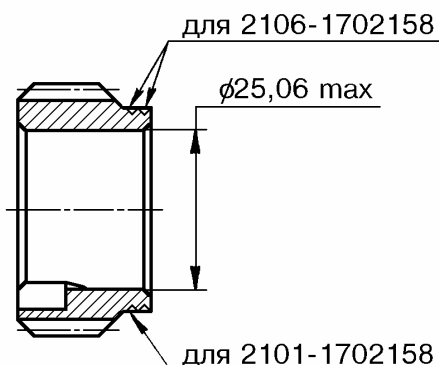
Шестерня ведущая привода спидометра – 2101-1702158, 2103-1702158, 2106-1702158.
